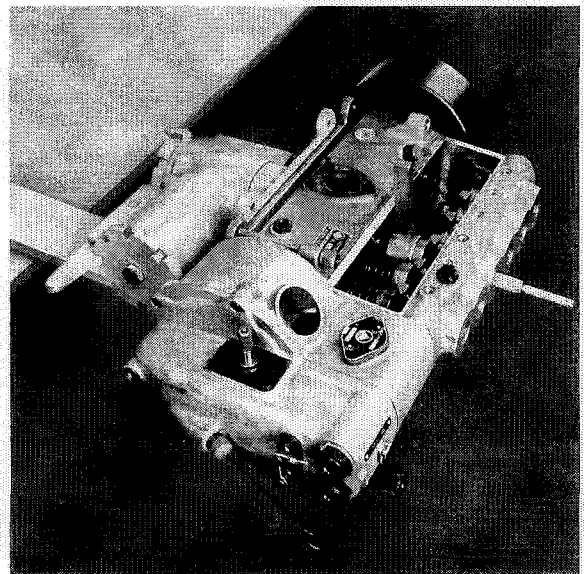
Einführen der Ausziehvorrichtung für die Pumpenelemente
